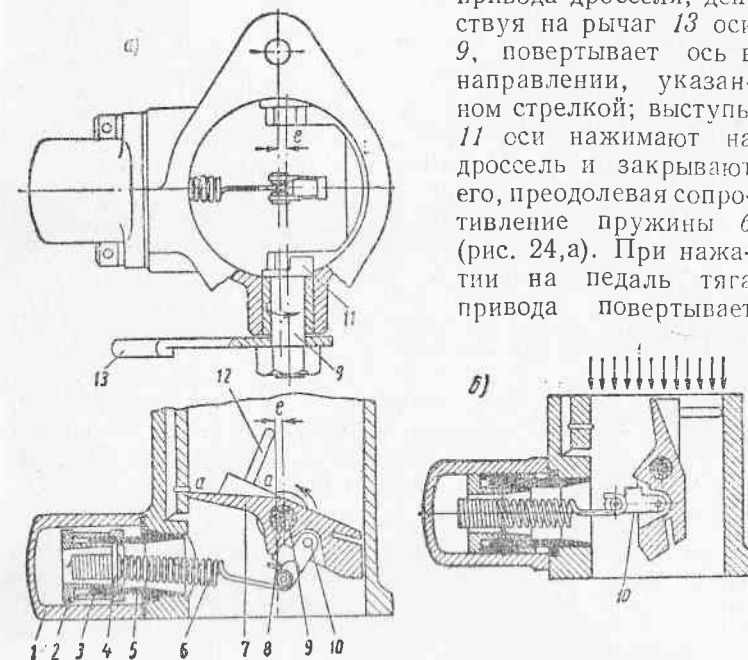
Ограничитель максимального числа оборотов коленчатого вала двигателя ГАЗ-51А.
